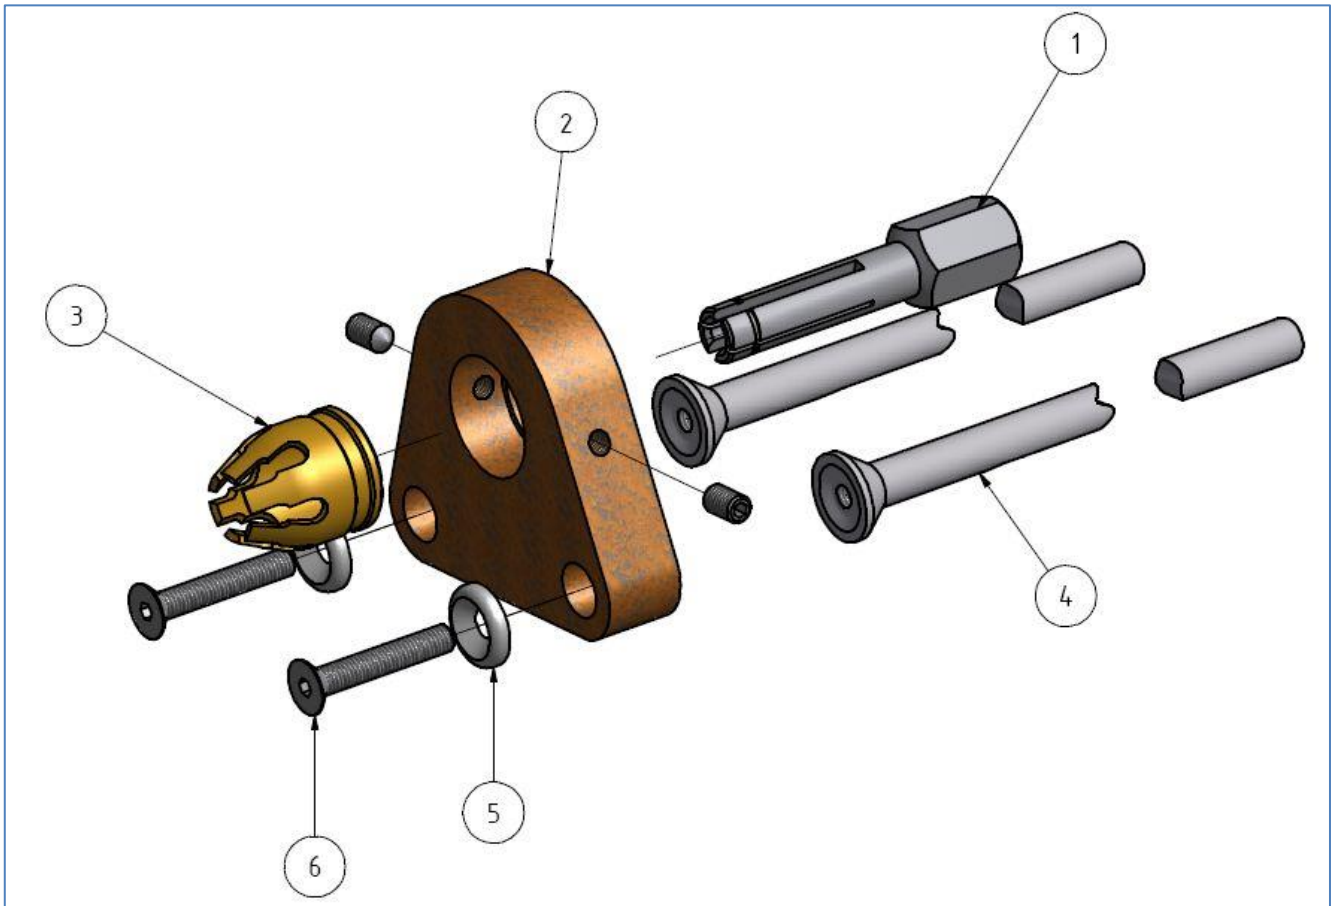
Stützeinrichtung zum Schweißen von Faserfix-Stiften Ø 5, Länge L
